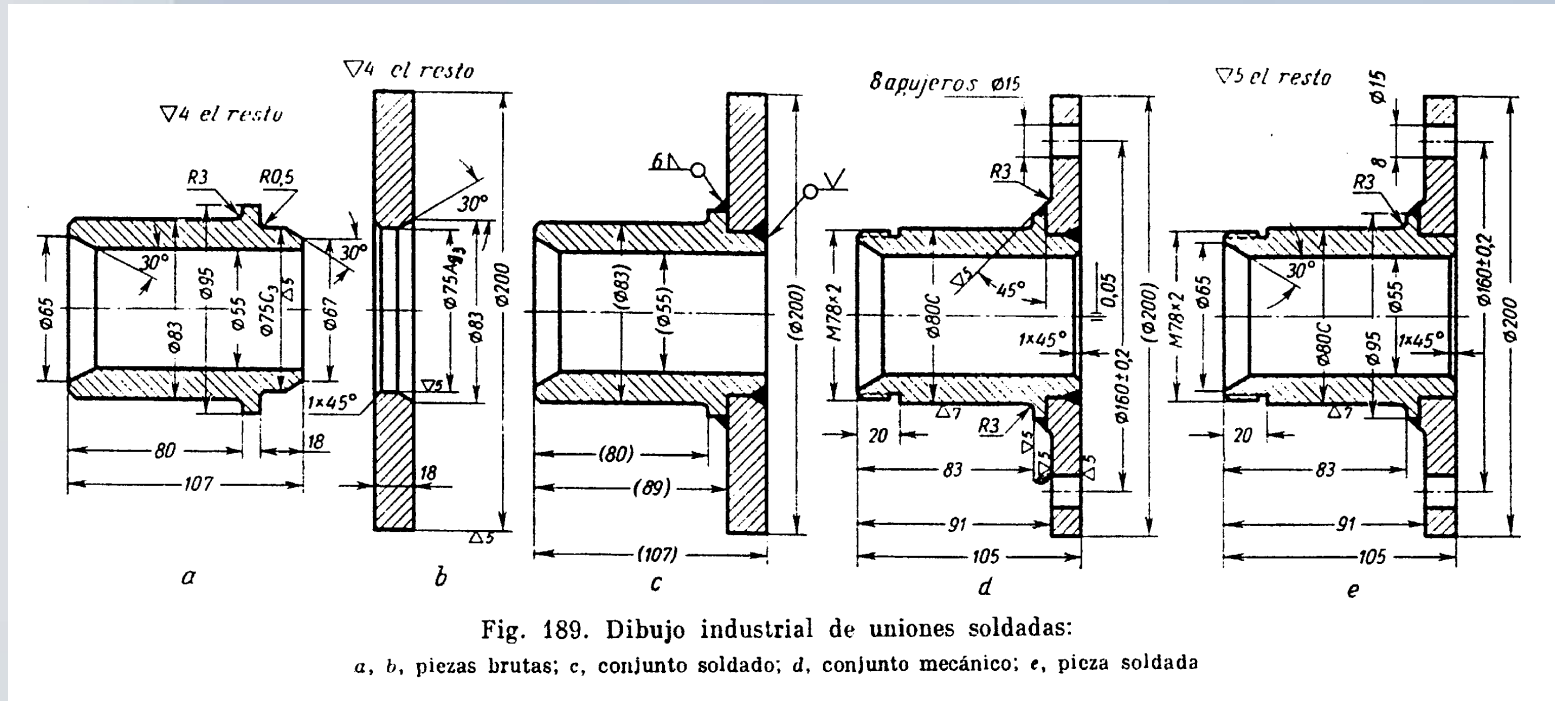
Dibujo industrial de uniones soldadas:
